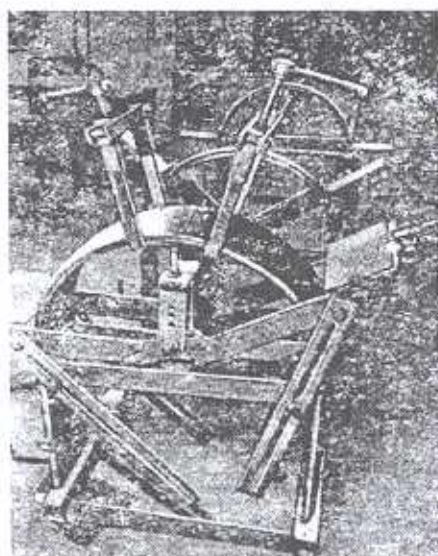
Облегченный шаблон для сборки и пайки катушек
